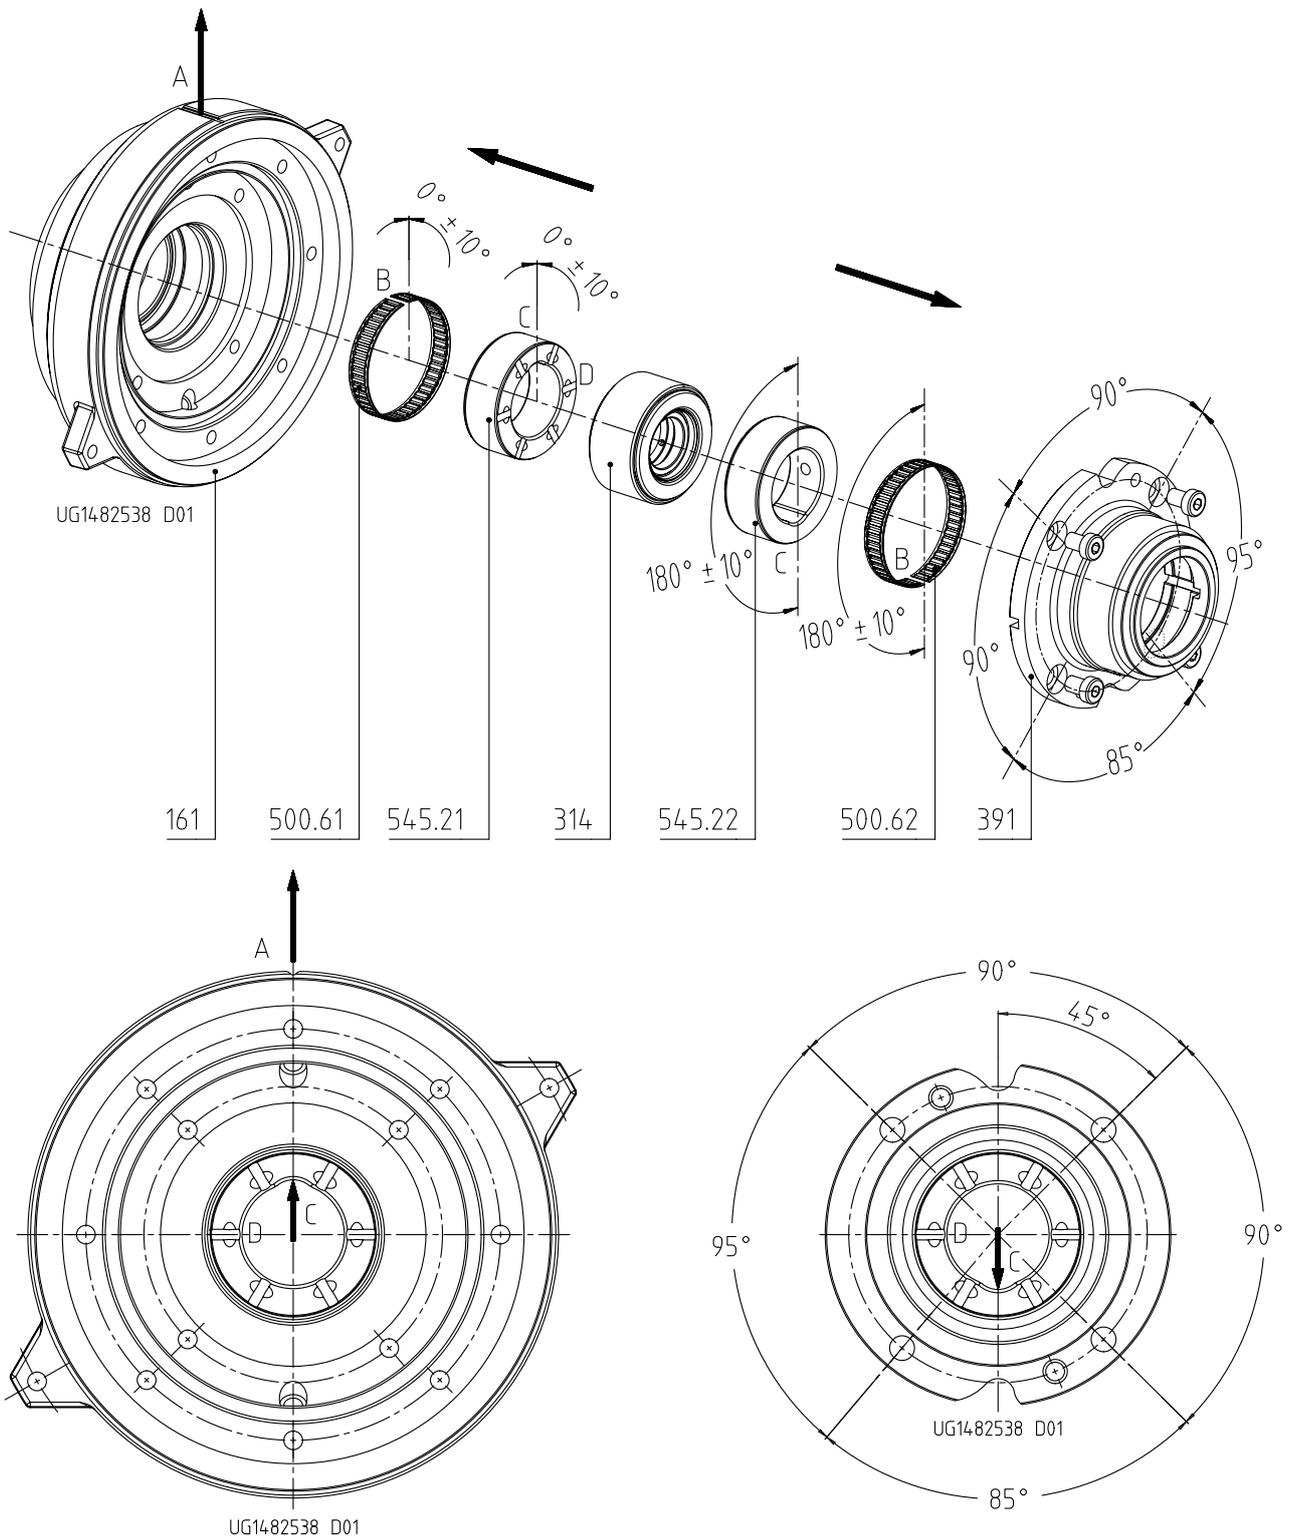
Posizione degli elementi di serraggio e bussole del cuscinetto con supporto CS40 / CS50 / CS60
